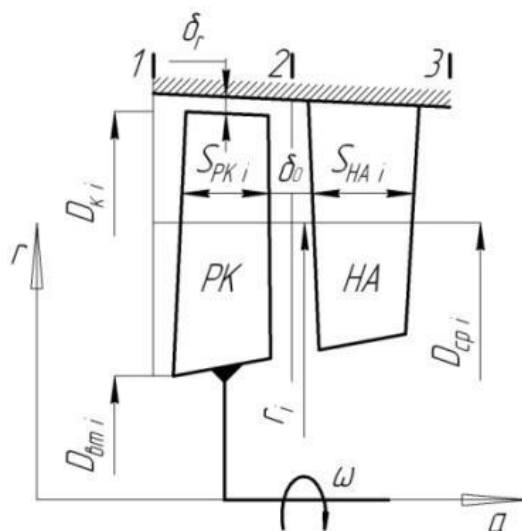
Схема и основные геометрические параметры ступени осевого компрессора
